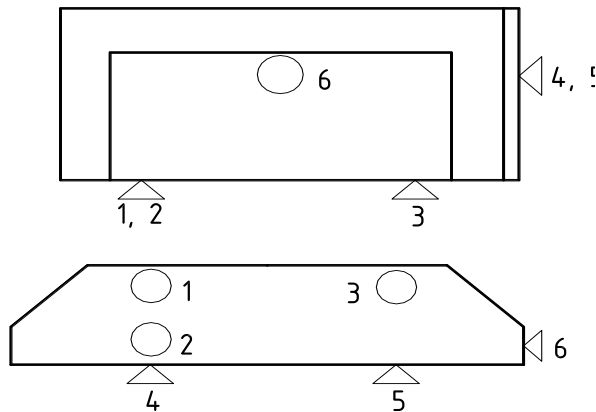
Схема встановлення заготовки при обробленні площини 290×60.
